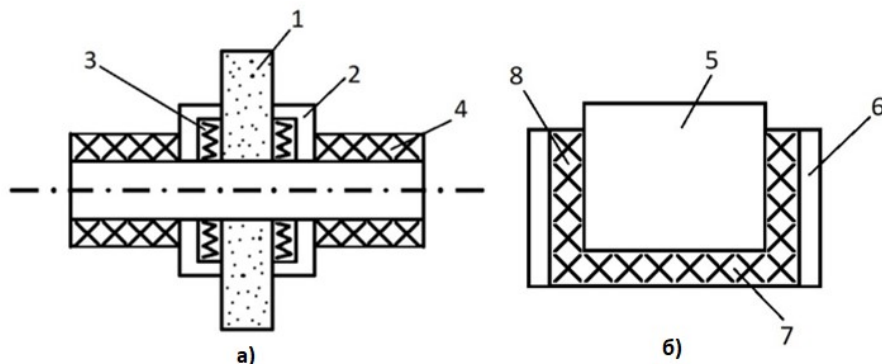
Системы снижения шума узла резания и заготовки профильно-шлифовального станка: 1 - шлифовальный круг; 2 - корпус и стеклотекстолита (толщина 2-3 мм); 3 - вибропоглощающие элементы из магнитопласта толщиной 5-6 мм; 4 - резиновые шайбы (резина марки 1002 толщиной 8 мм на сторону), устанавливаемые на оправку шлифовального круга; 5 - шлифуемое изделие; 6 - губки тисков; 7 и 8 - пластины из стеклотекстолита толщиной 5-6 мм
